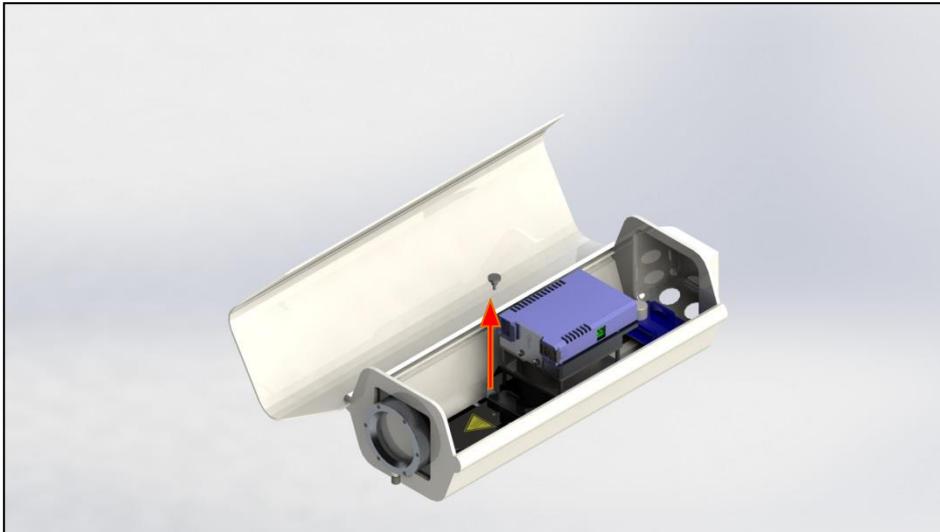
Lösen der Rändelschraube vom Befestigungsblech
